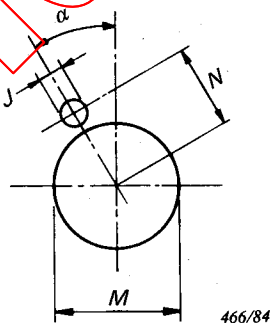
Dimensions essentielles pour la découpe du panneau.
